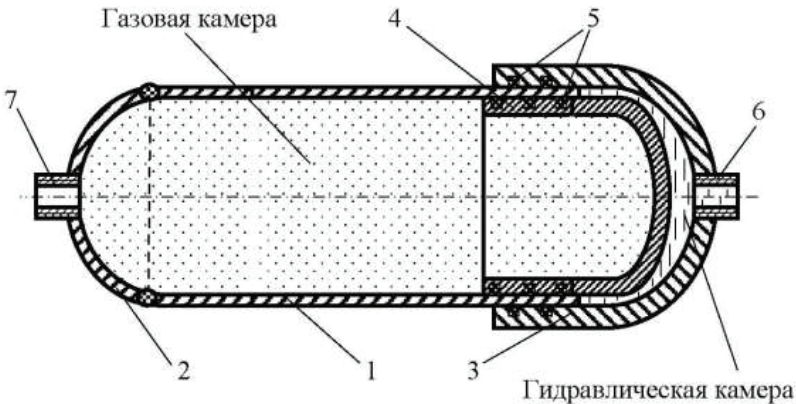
Принципиальная схема гидроаккумулятора, где 1- корпус; 2- днище; 3- крышка; 4- поршень; 5- уплотнительное кольцо; 6,7- наплыв
